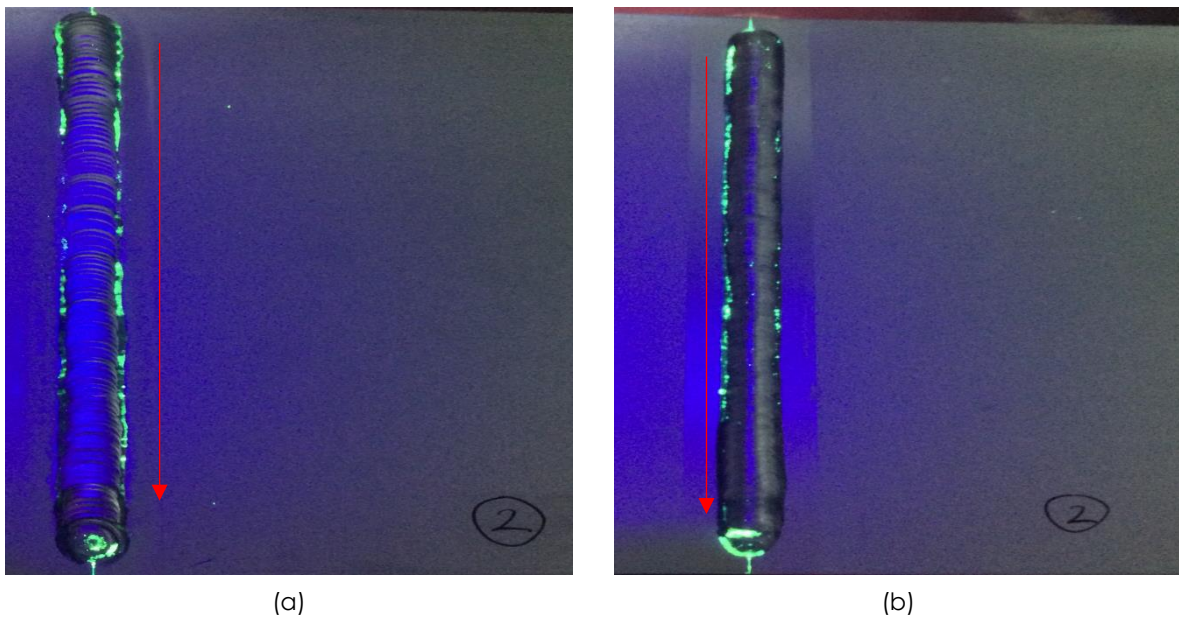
(a) Cordón Soldadura Superior Probeta 2. (b) Cordón de Soldadura Inferior Probeta 2.
